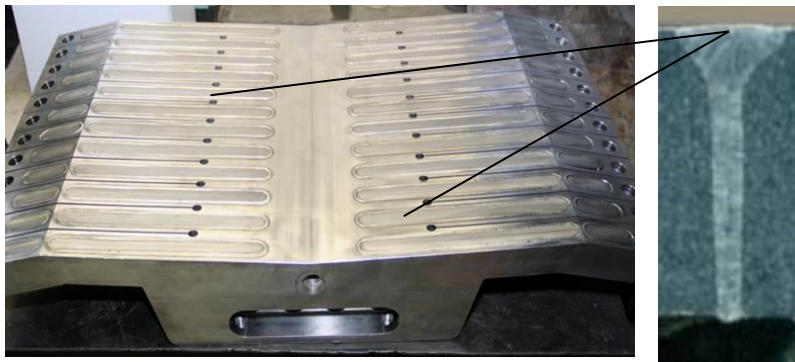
Внешний вид несущей конструкции первой стенки ИТЭР и поперечный макрошлиф шва
